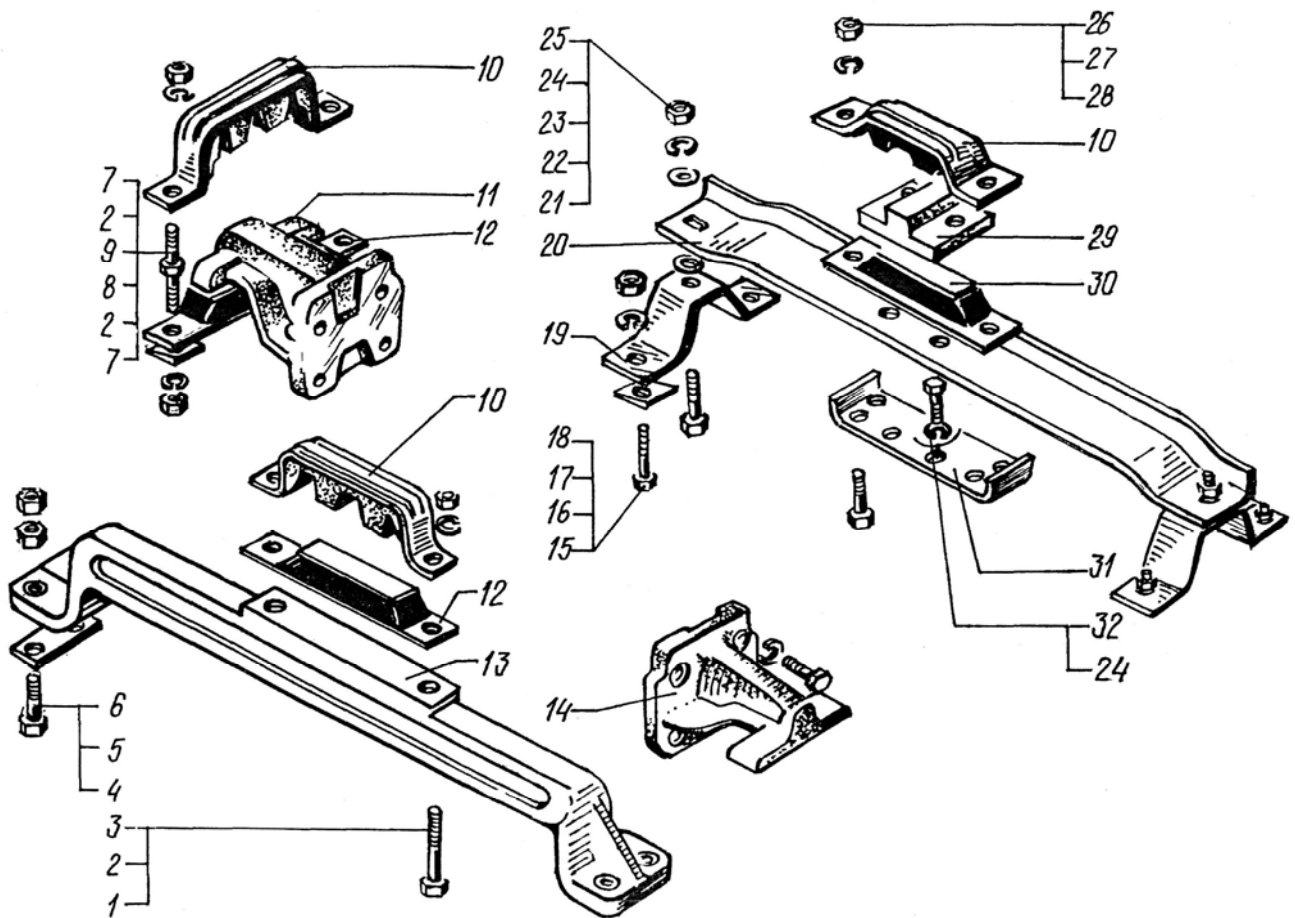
Крепление силового агрегата на раме с коробкой передач ЯМЗ-2381-31:
